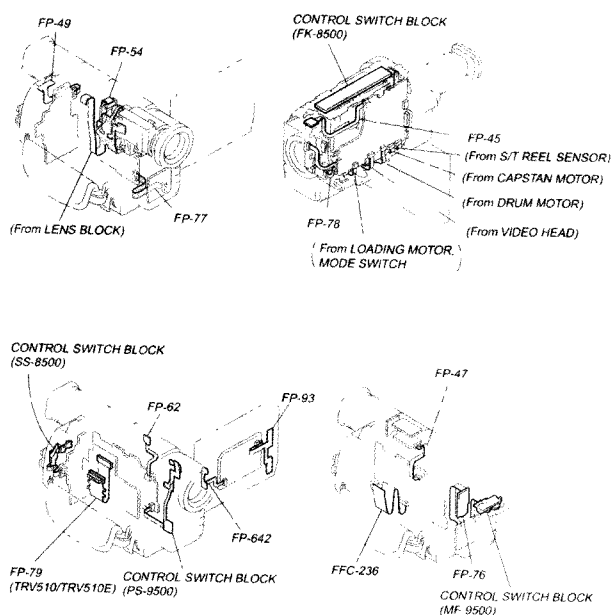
Расположение соединительных шлейфов в корпусе видеокамер
